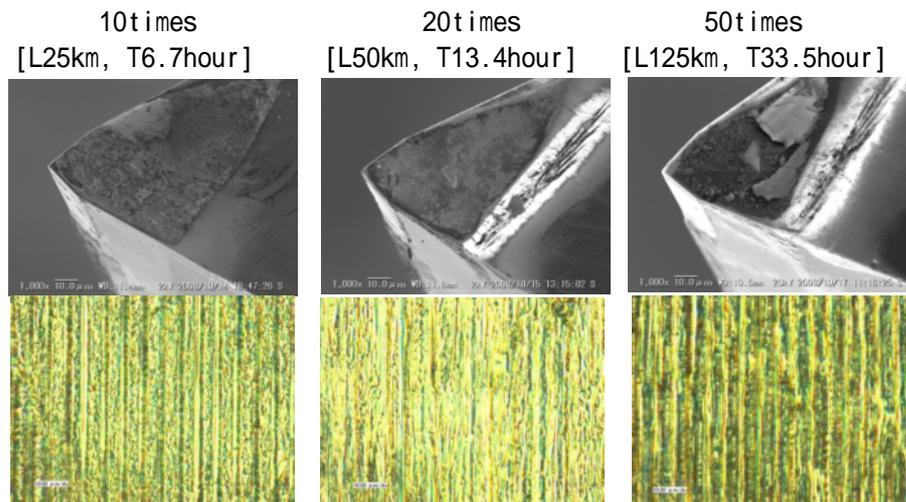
[Tool 3]の工具摩耗と加工面性状
